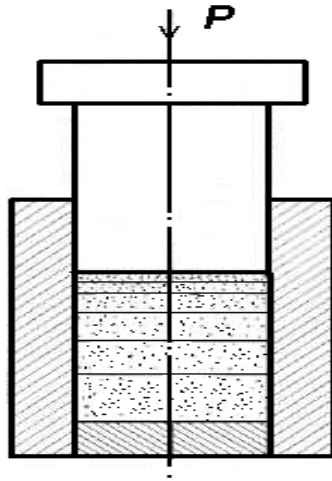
Колба - втулка з циліндричним стрижнем (лабораторний стенд, який реалізує експеримент)
